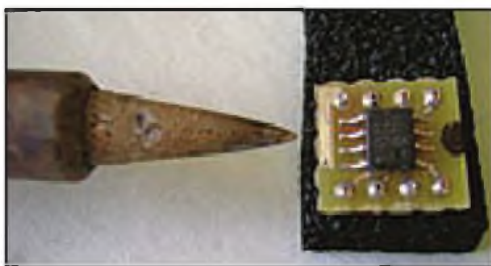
Foto I. Una vista ampliada del soldador de punta fina de W5SUJ para el montaje de los componentes superficiales. Obsérvese su tamaño comparado con el de las patillas del integrado SMD. Chuck insiste en que el montaje de estos componentes requiere el desarrollo de una nueva habilidad, evitando puentes de soldadura entre conexiones y practicando con montajes más complejos cada vez.
